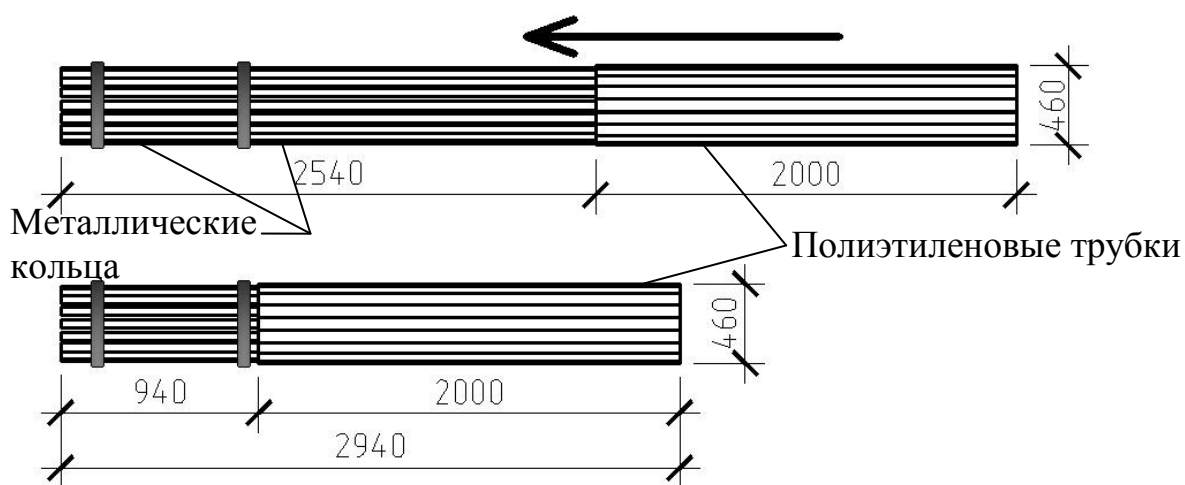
Размеры конструкции с выдвинутыми телескопическими трубками и в положении для транспортировки.
